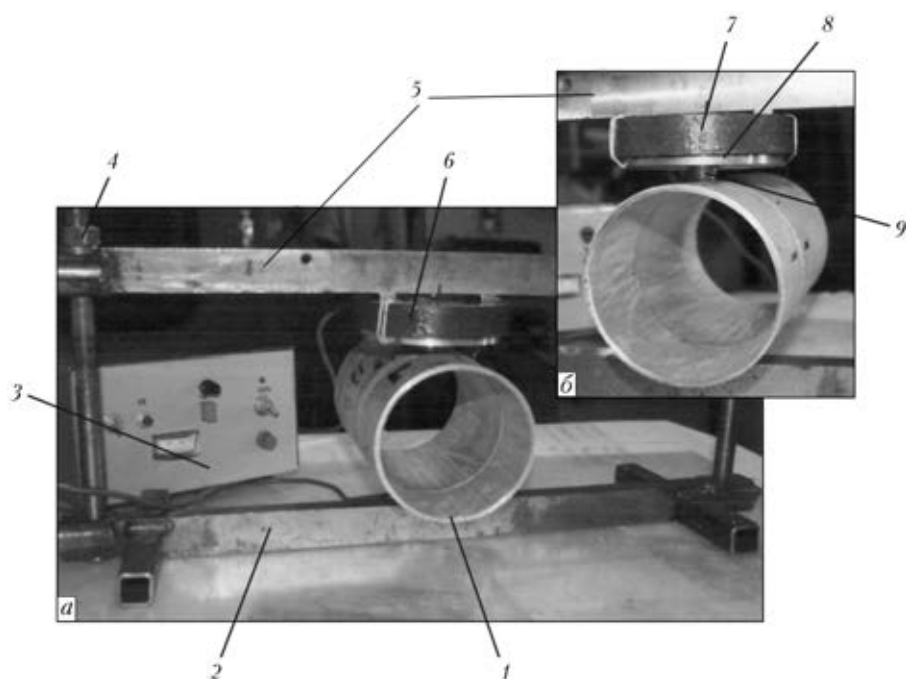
Сборочное устройство для ЭДО сварных кольцевых соединений из сплава АМг6 (а) и позиционирования индуктора (б): 1 — образец; 2 — балка опорная; 3 — источник питания ЭДО; 4 — шпилька направляющая с нагружающей гайкой; 5 — балка прижимная; 6 — индуктор; 7 — катушка индуктивности; 8 — диск; 9 — электрод
